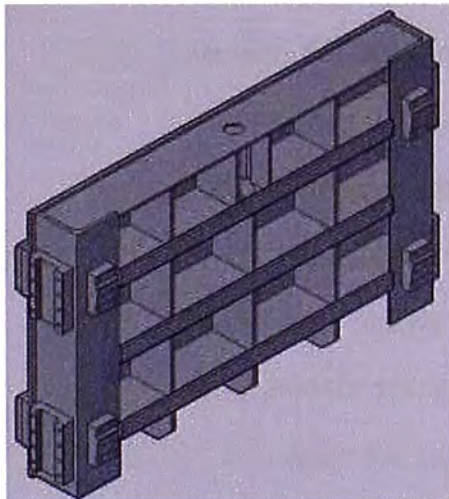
Arreglo 3D de compuerta plana deslizante
